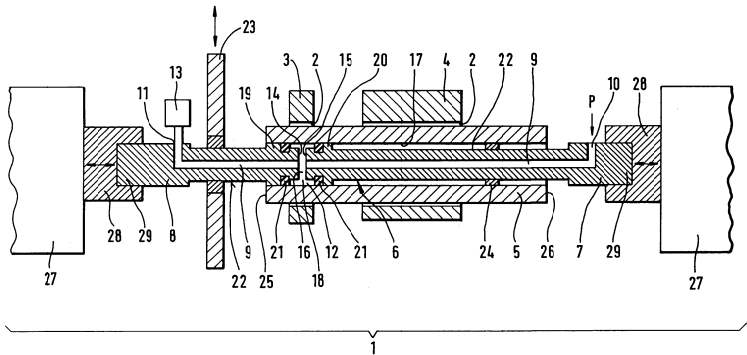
geteiltes Werkzeug zum Innenhochdruckfügen /6/
